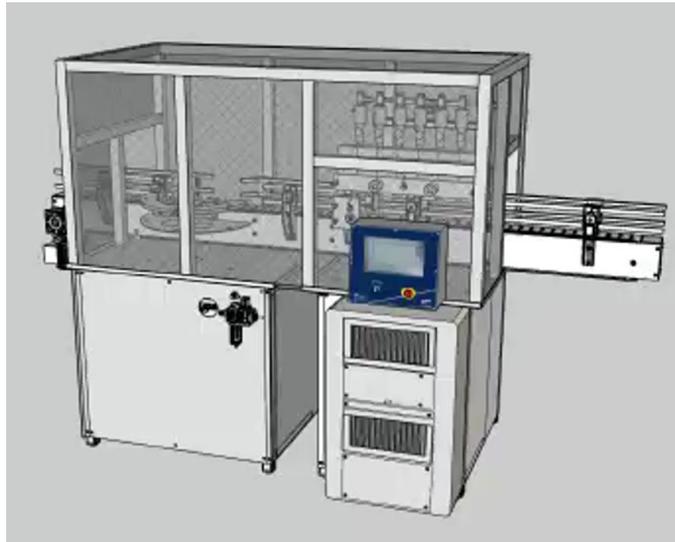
DISEÑO DE CABINA DE MÁQUINA DE PRODUCCIÓN.
